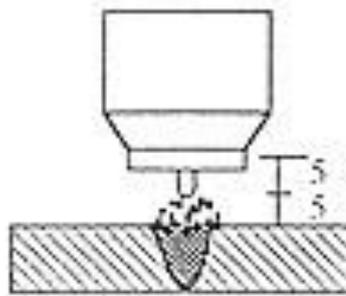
Distancia mínima necesaria en Soldadura TIG. [23]
